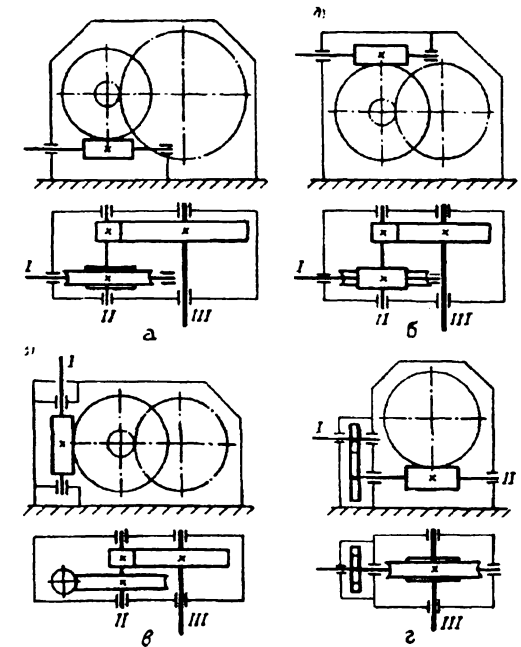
Кинематические схемы двухступенчатых червячно-цилиндрических (а...в) и цилиндрично-червячного (г) редукторов:
